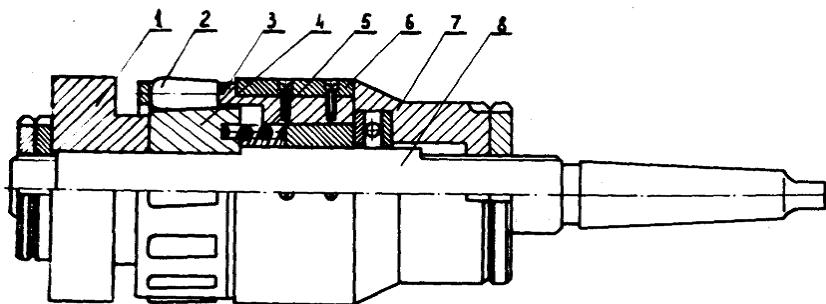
Конструкция усовершенствованной многороликовой раскатки
